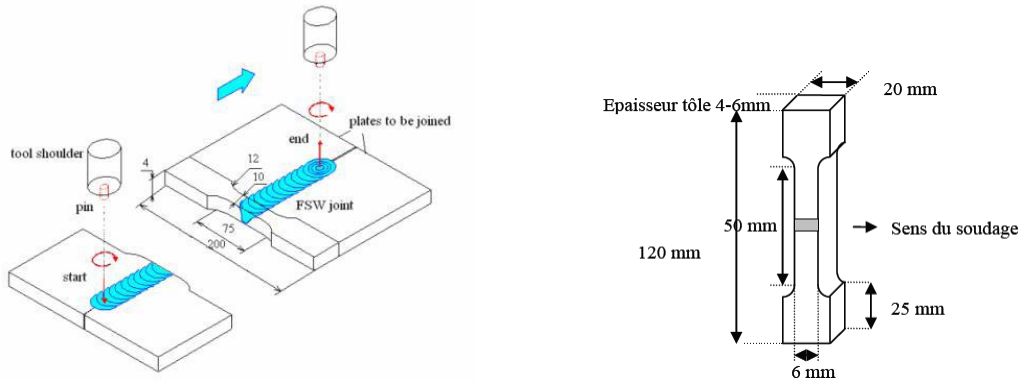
Forme et dimensions d'une éprouvette prélevée perpendiculairement à la direction du soudage. La soudure est représentée par la zone grise [2].
